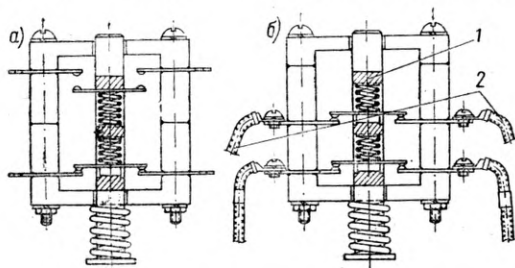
Схема блокировочного устройства пускового контактора Д1 типа КПВ-504:
